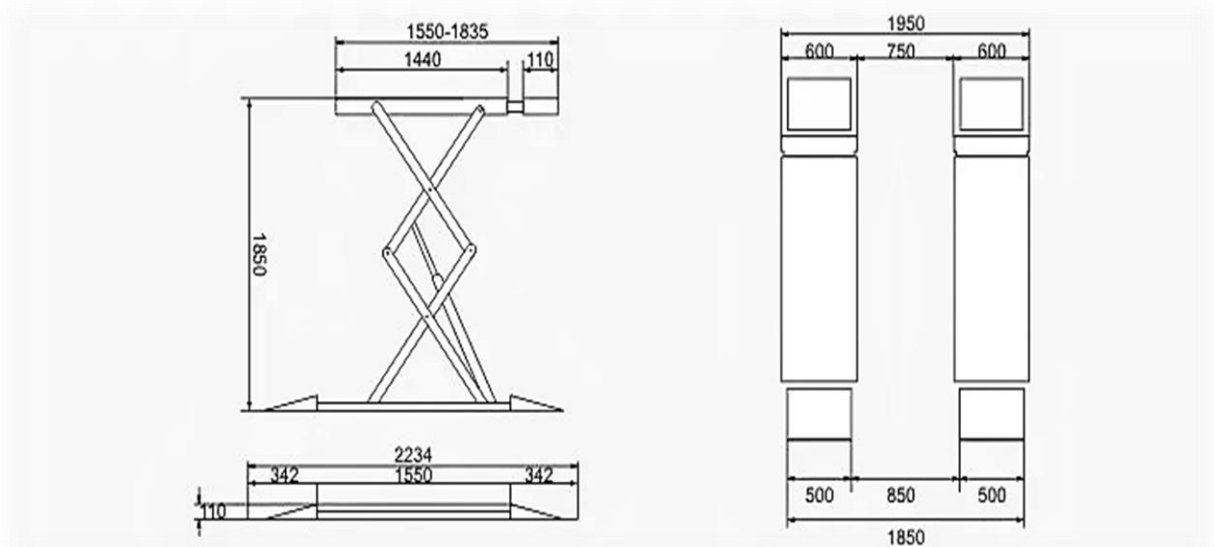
схема ножичного підіймача SkyRack 3030
